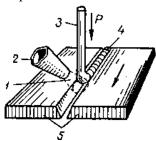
Схема сварки нагретым газом с применением присадочного материала:
